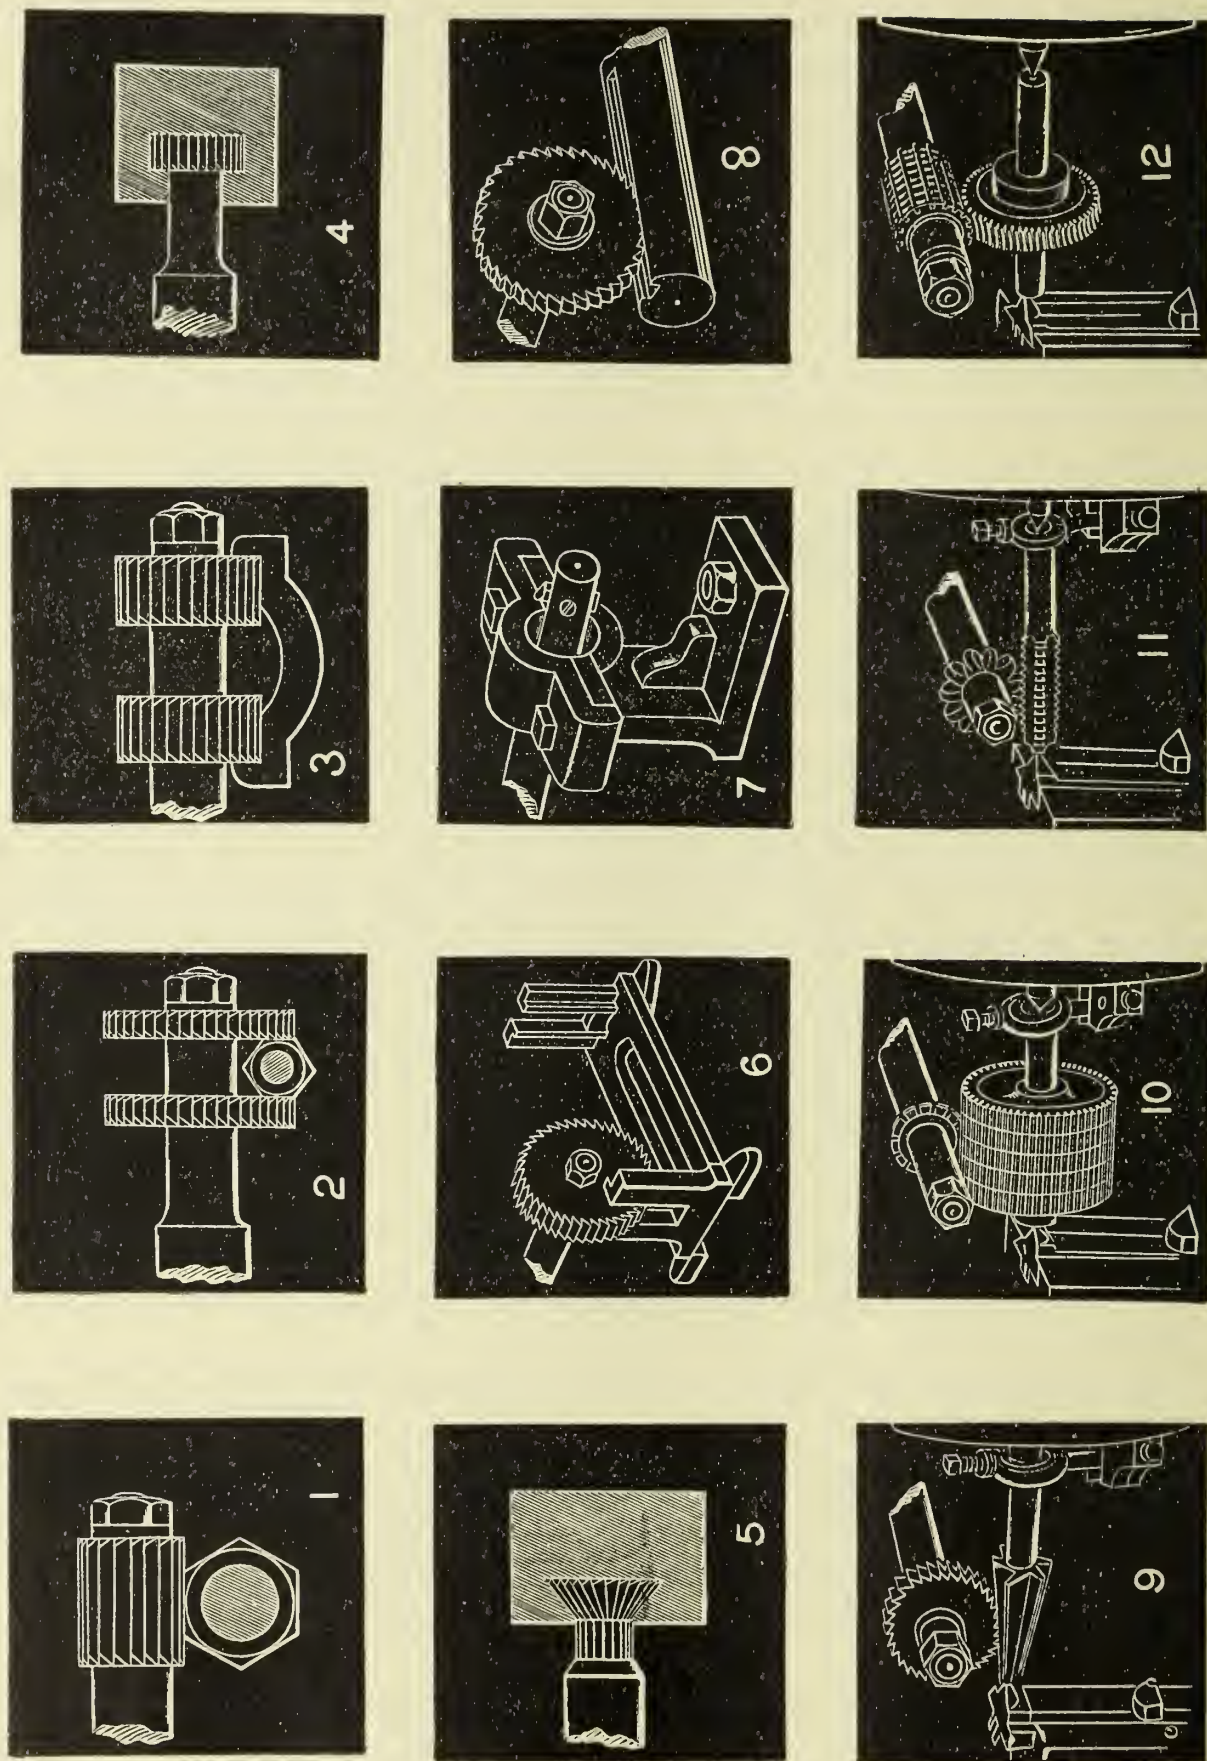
Ausführung verschiedener Fräs- und Bohrarbeiten.
